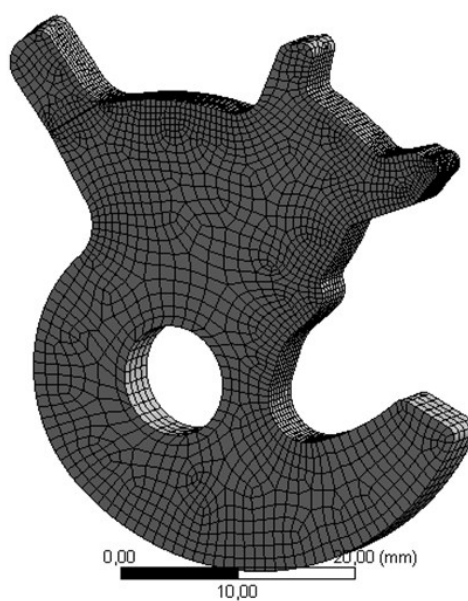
Zadání funkce „Face Sizing“ u rohátky X152 (test 1)
